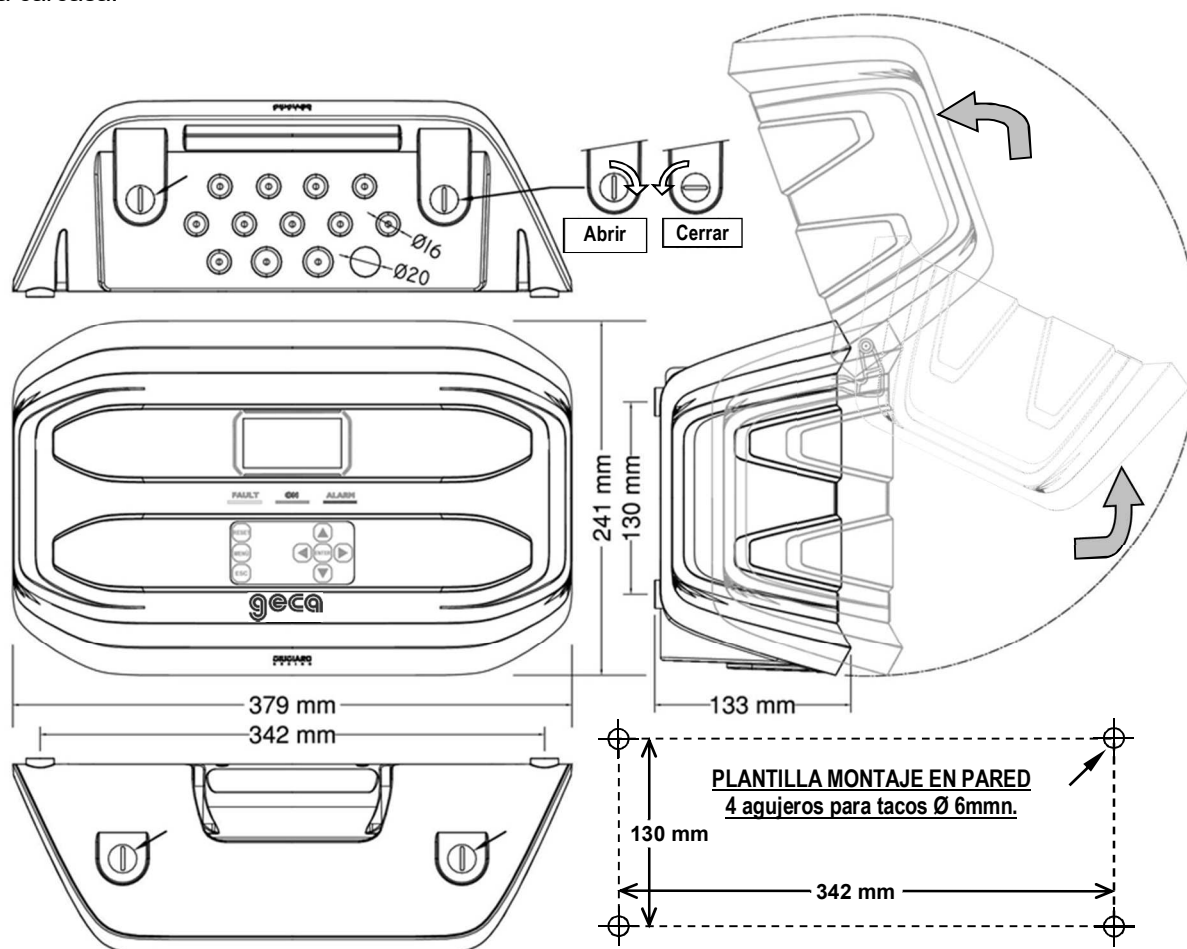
CE408 Dimensiones y plantilla de montaje en pared
